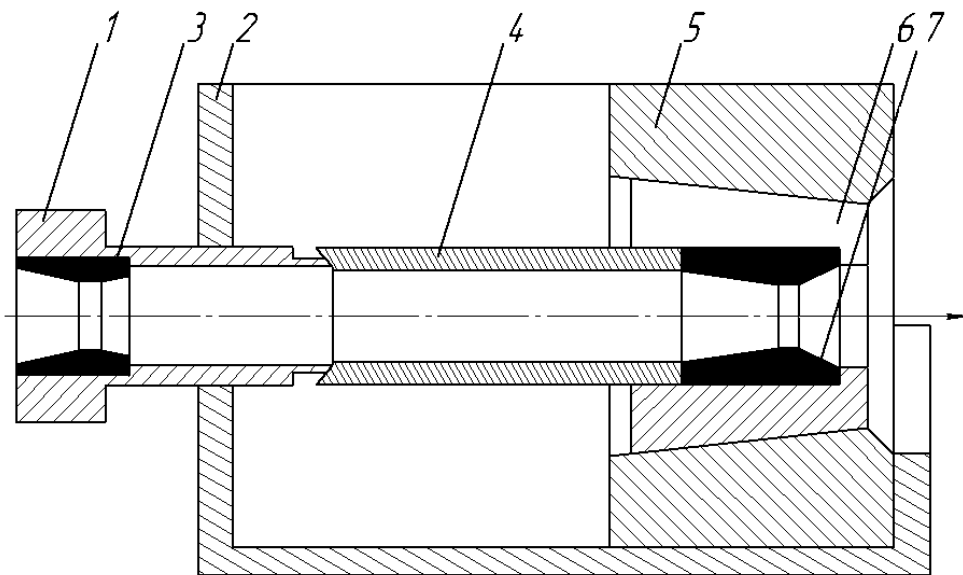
Складений інструмент: 1 - затискний гвинт; 2 - волокотримач; 3 - напірна волока; 4 - напірна втулка; 5 - корпус; 6 - затискна (цангова) втулка; 7 - робоча волока.
